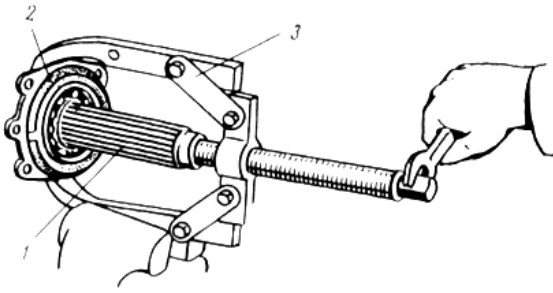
Випресування первинного вала: 1- первинний вал; 2- стакан; 3- знімач
